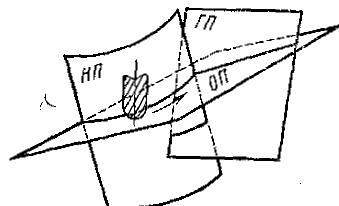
Обрабатываемая, направляющая и ограничивающая поверхности
